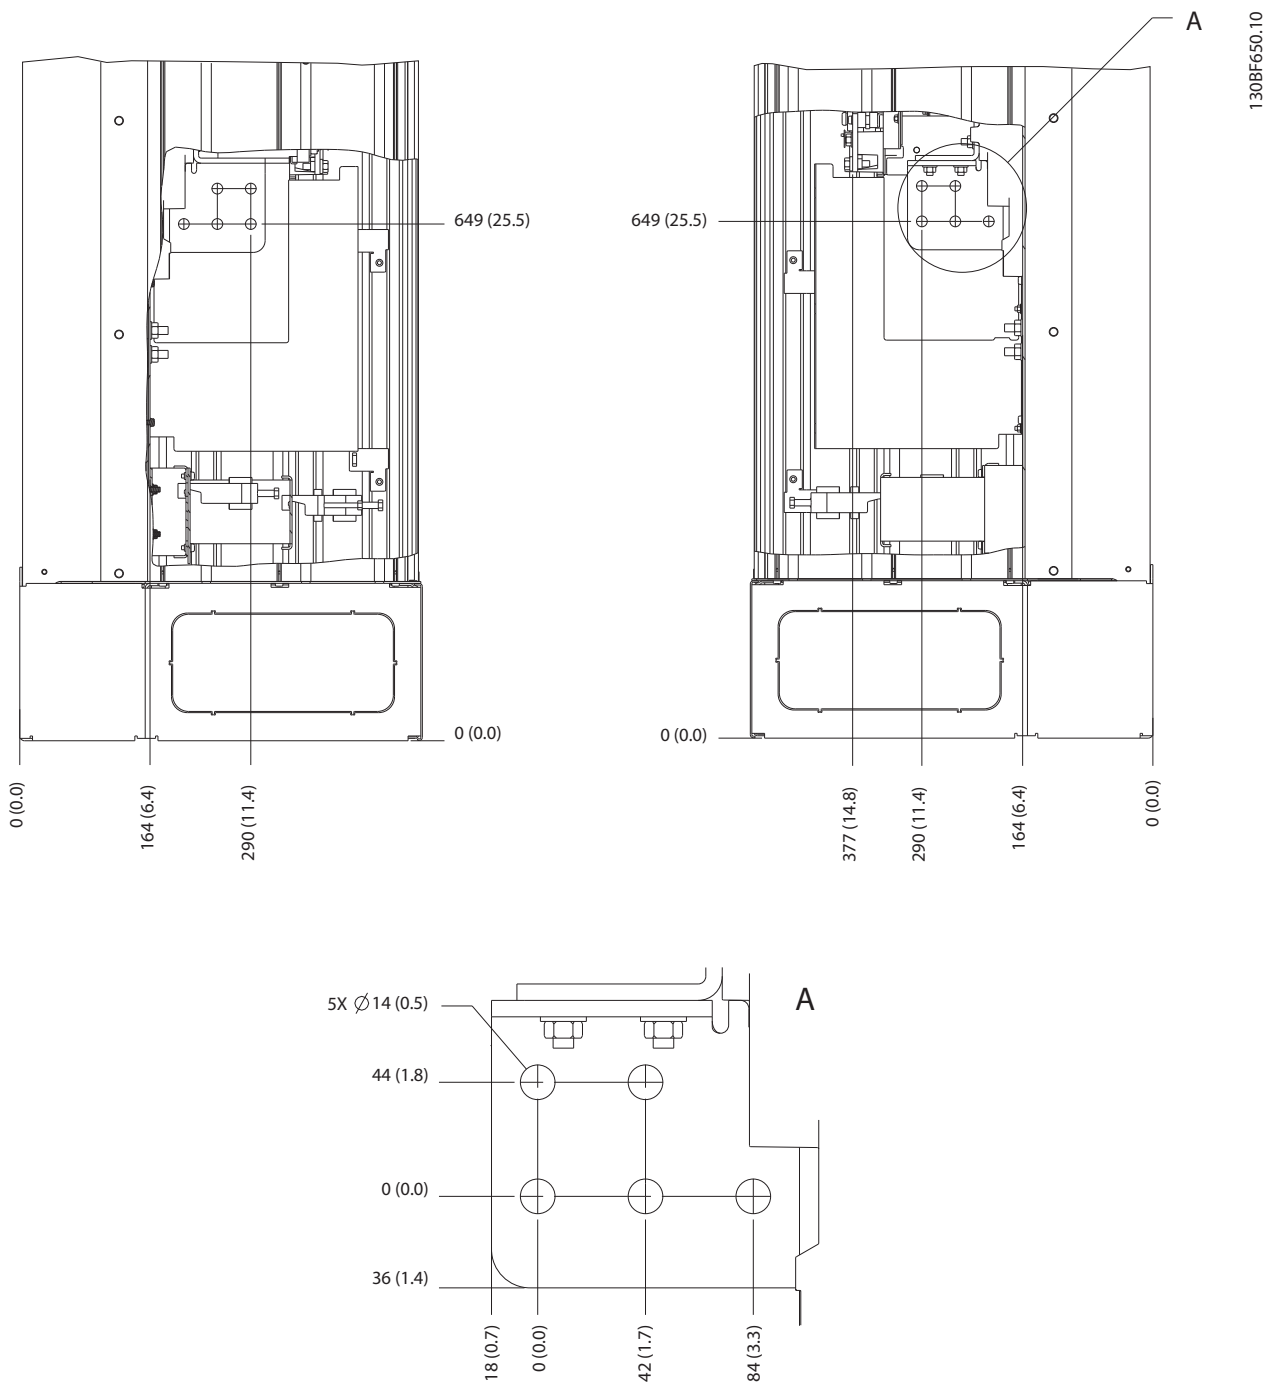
Размеры клемм корпуса E1h (вид сбоку)
